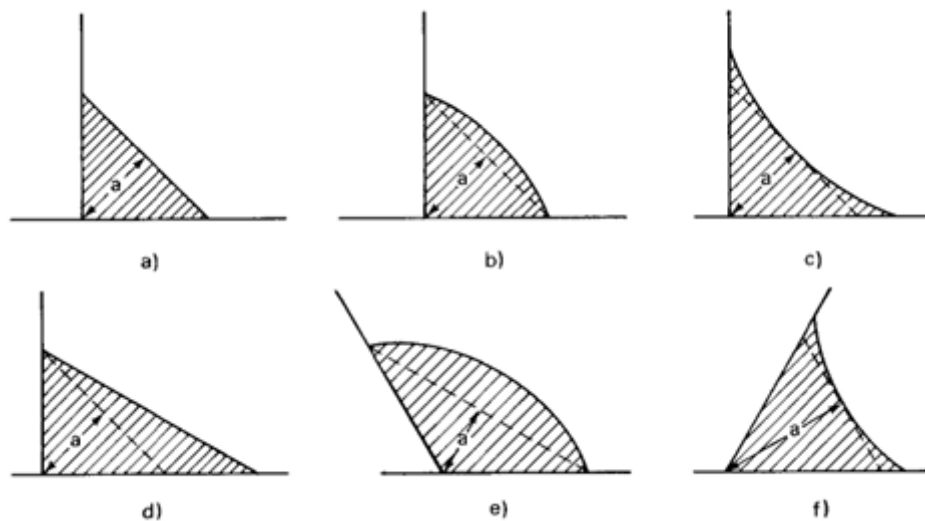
Altezza di gola definita per varie forme del cordone di saldatura.
